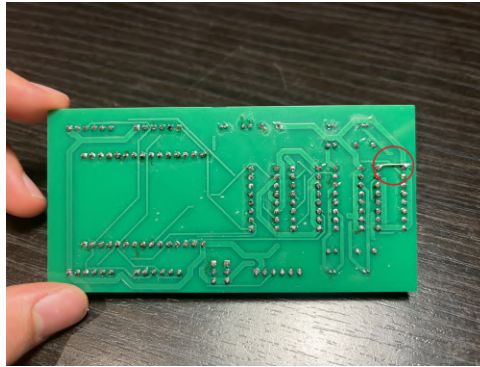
Fotografia de la soldadura per solucionar l'error. Font: Elaboració pròpia
